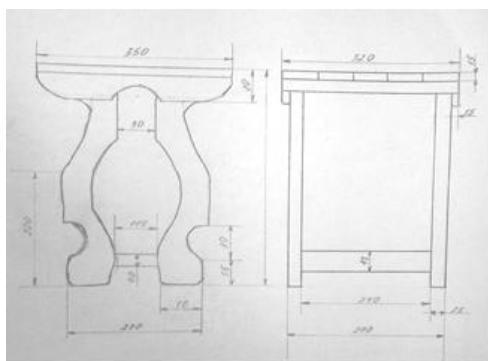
Изготовление табурета по готовому чертежу. Масштаб 1:1
